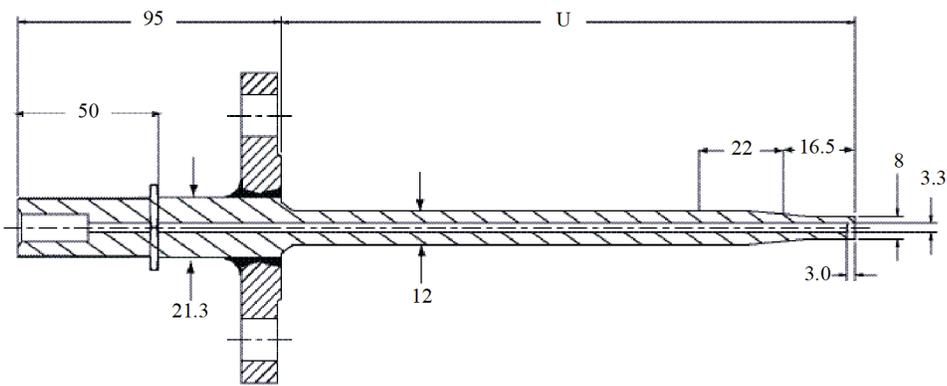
Schutzrohr aus Vollmaterial mit Flansch (6 mm)
